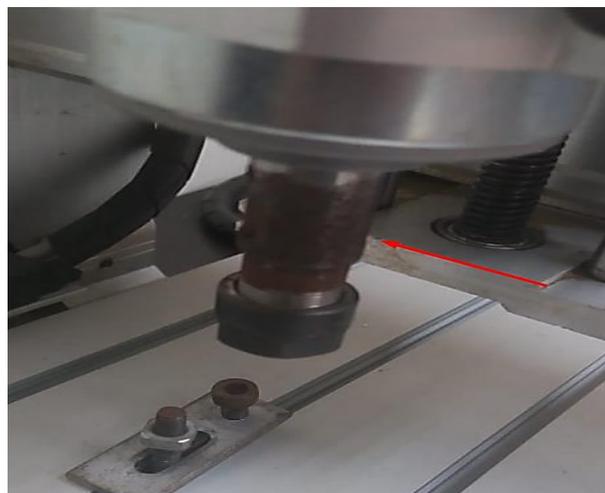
Corrosión en el accesorio de husillo de la mini CNC.
